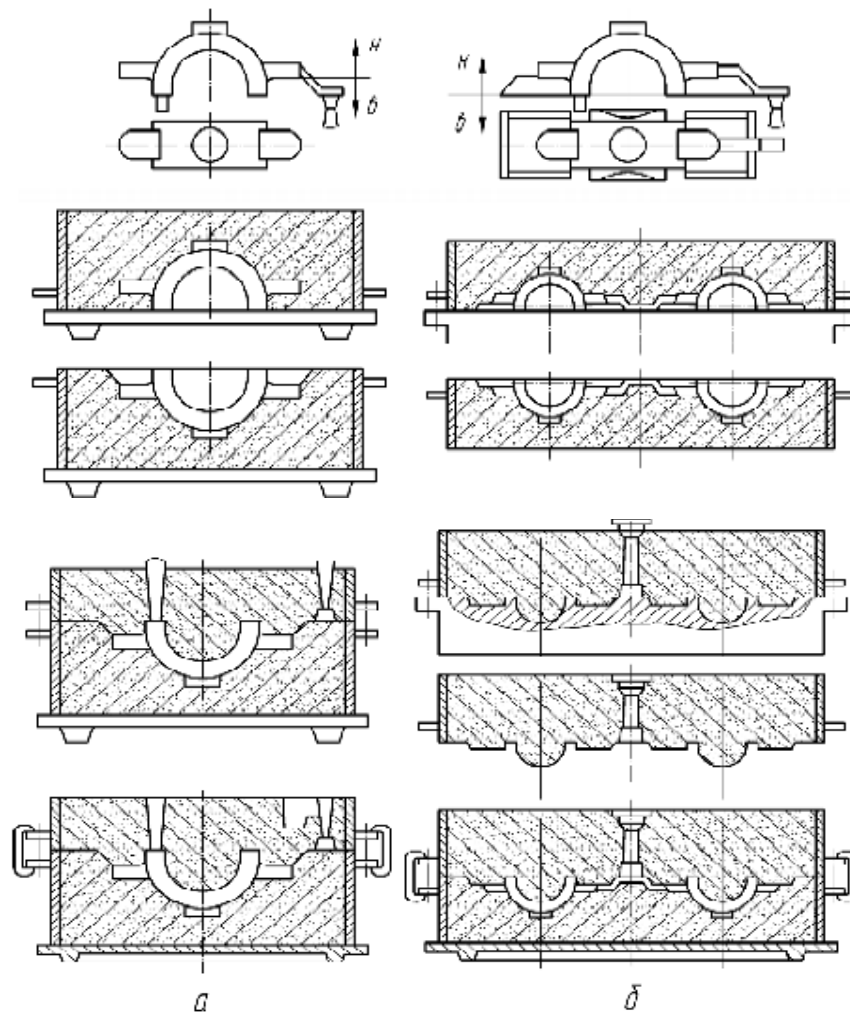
Схемы изготовления формы для получения отливки крышки подшипника вручную (а) и на машинах (б)
